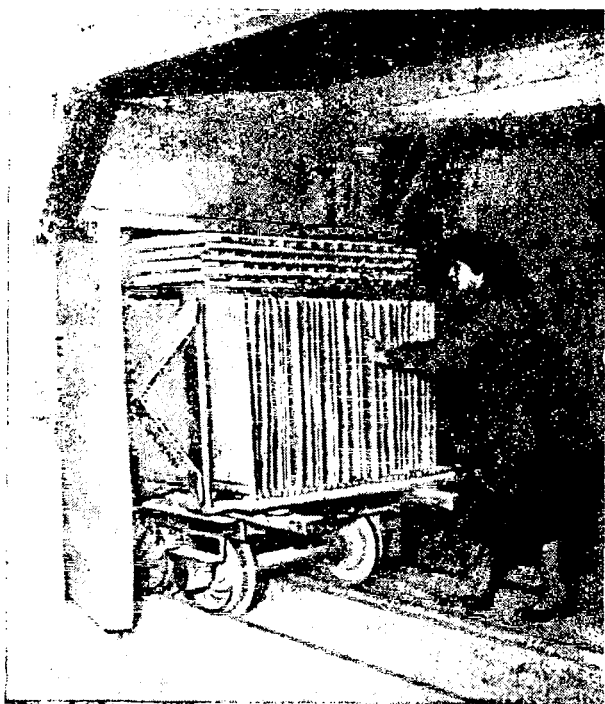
Вагонетка с плитами гипсовой штукатурки (загрузка сушилки)
